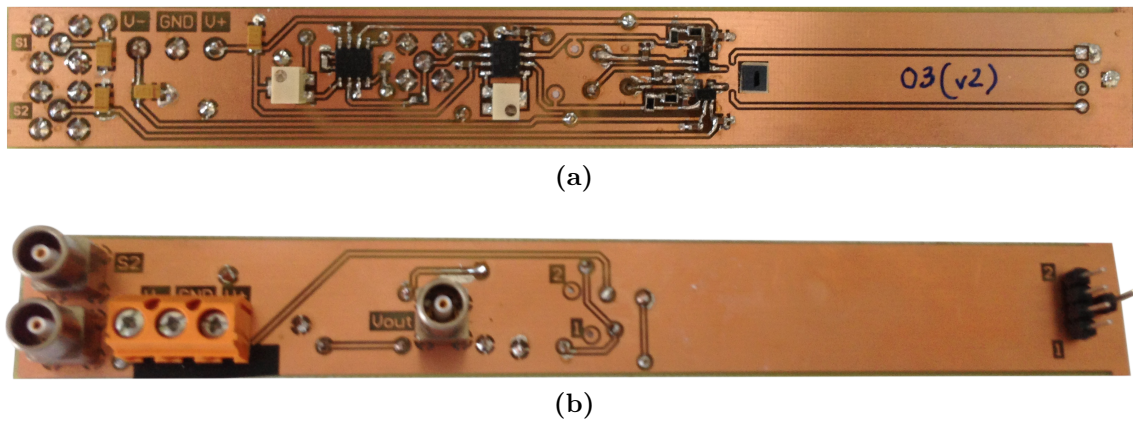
Layout per la stampa della PCB (a) vista dal basso, (b) vista dall'alto
